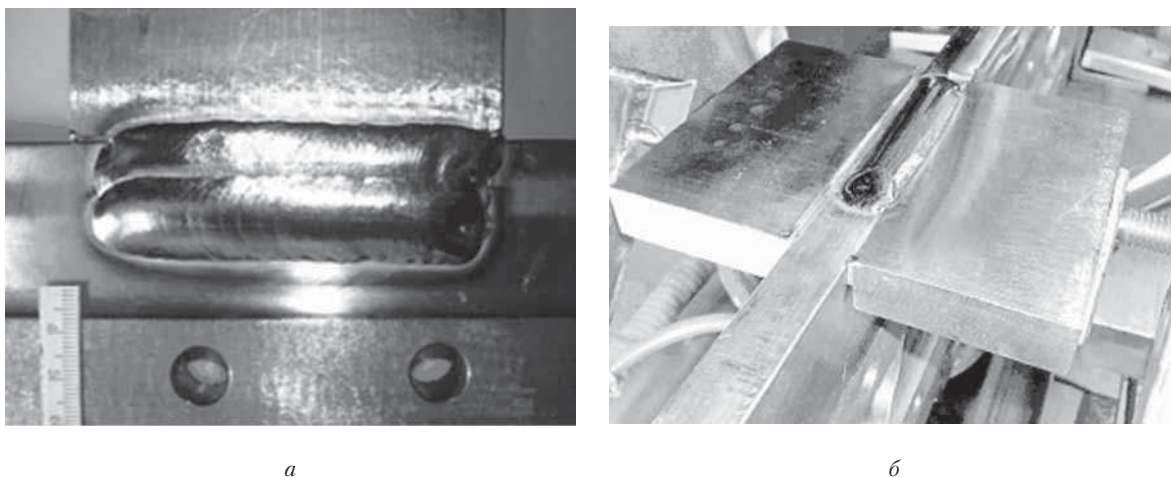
Зовнішній вигляд наплавлених ділянок рейки: плоскої (а) и торцевої (б)
